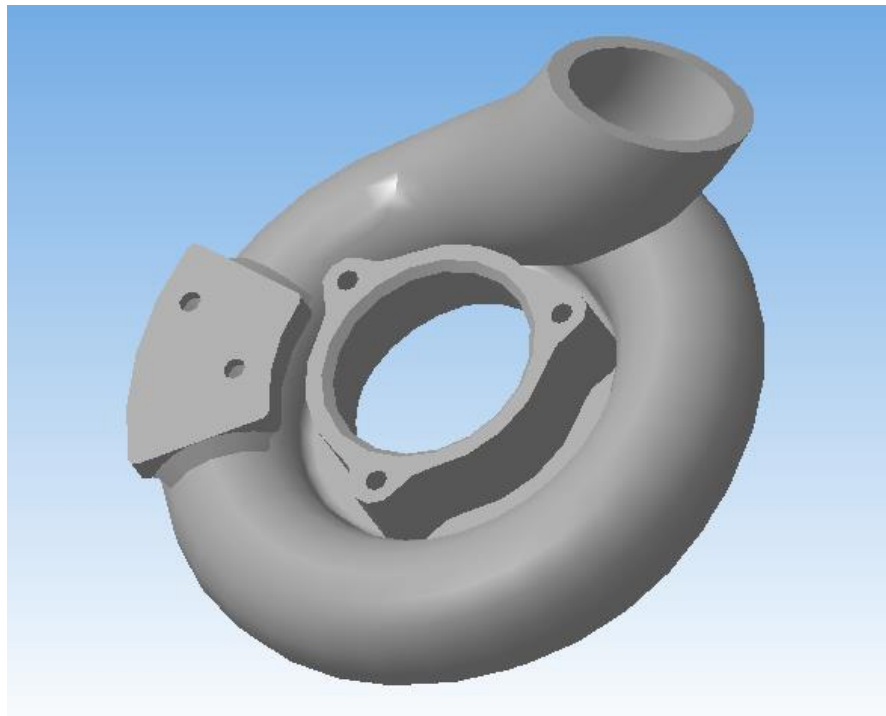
Тривимірна модель деталі «Корпус компресора»
